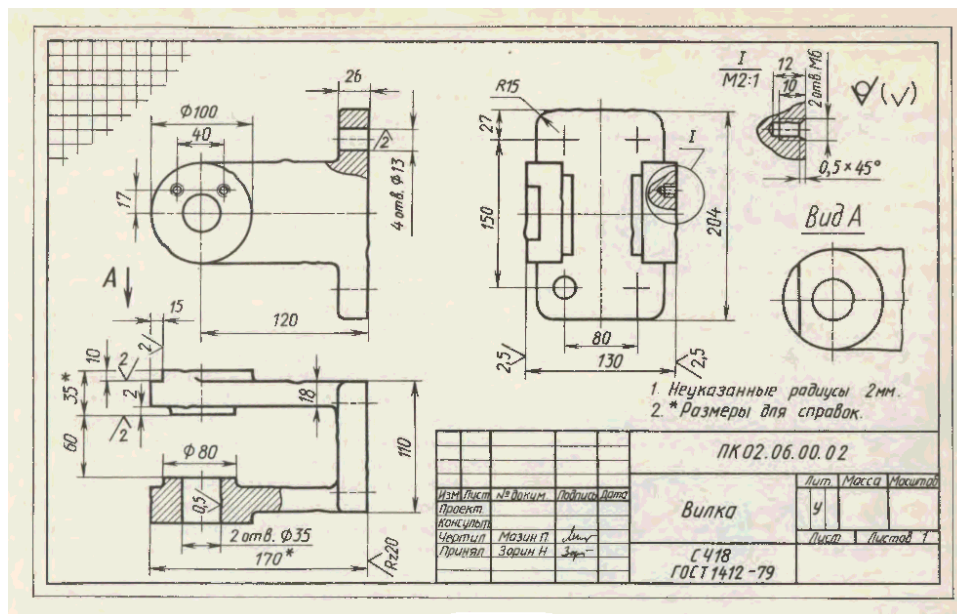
Пример выполнения эскизов деталей при детализации сборочного чертежа Блок направляющий
